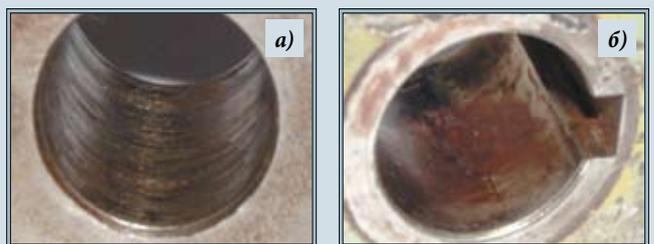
Состояние посадочных поверхностей зубчатого колеса и вала
